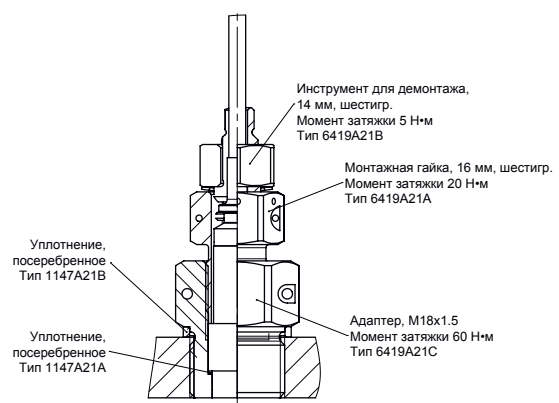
Установка датчика с помощью переходника Типа 6419A21C и инструмента для демонтажа Типа 6419A21B для датчика с использованием разъема LEMO или свободными концами
